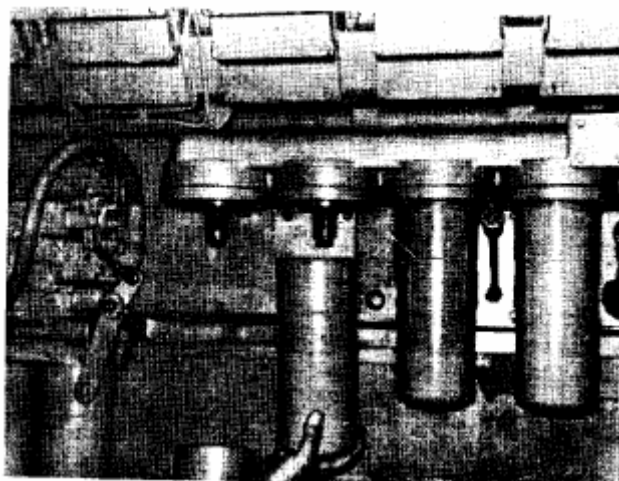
(K21907). Установка «центробежного» фильтра смазочного масла - двигатель КТ/КТА38.
